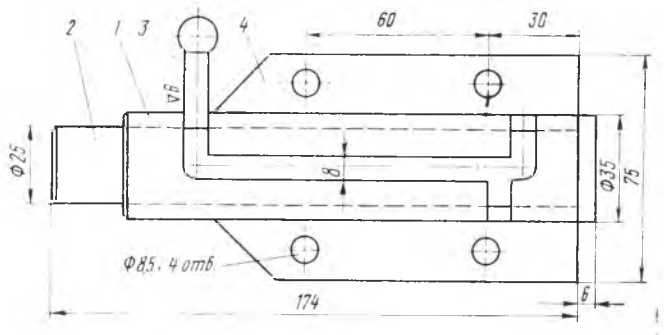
Схема шпингалетного упора к многошпиндельным сверлильно-присадочным станкам
